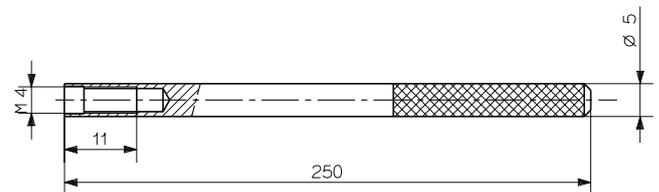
Ausziehwerkzeug für Blindsensor Typ 1319
